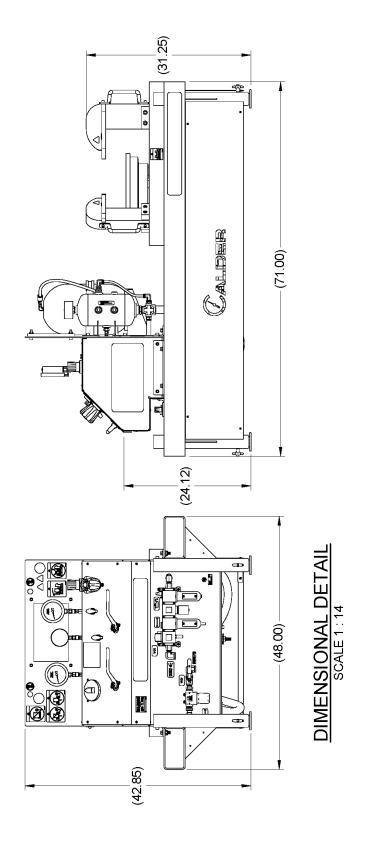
DIMENSIONES DEL TAT-SRV
